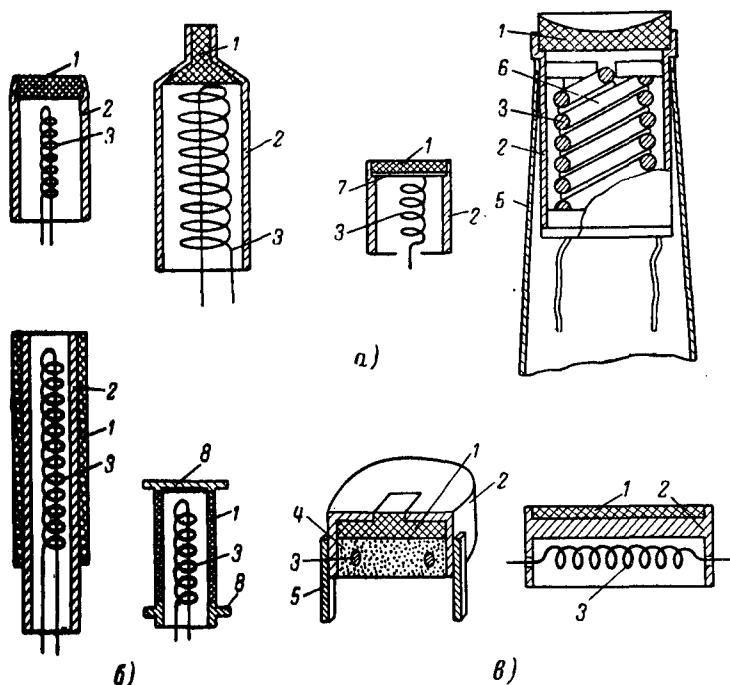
Конструкции прессованных и пропитанных катодов с плоской и сферической эмиттирующей поверхностью.
